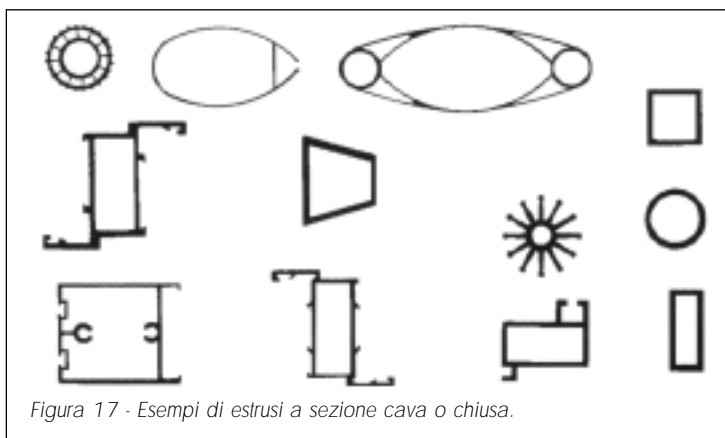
Esempi di estrusi a sezione cava o chiusa.
